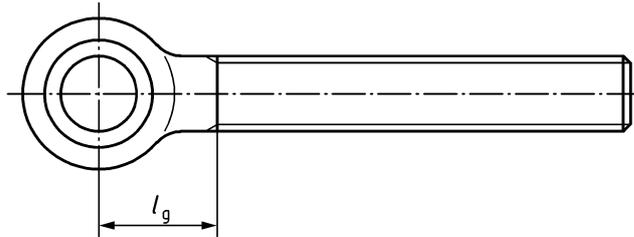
Augenschrauben mit Gewinde annähernd bis Auge
